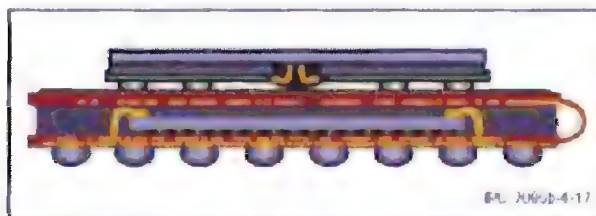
Корпус BGA со сложенными и собранными в пакет кристаллами
